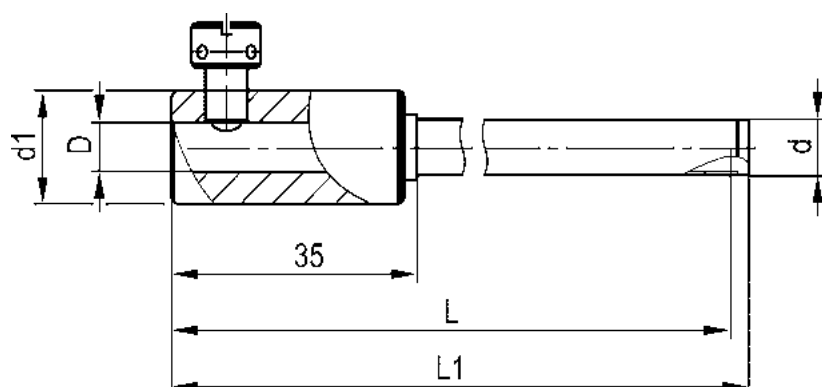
Гильза цилиндрическая сварная со стопорным винтом с варным присоединением OS4
